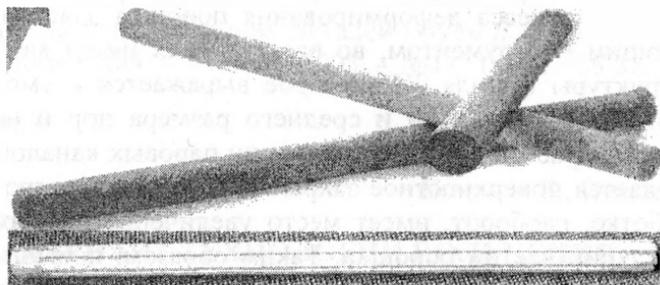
Вид прессовок с гладкой поверхностью и КПС со сформованными паровыми каналами
